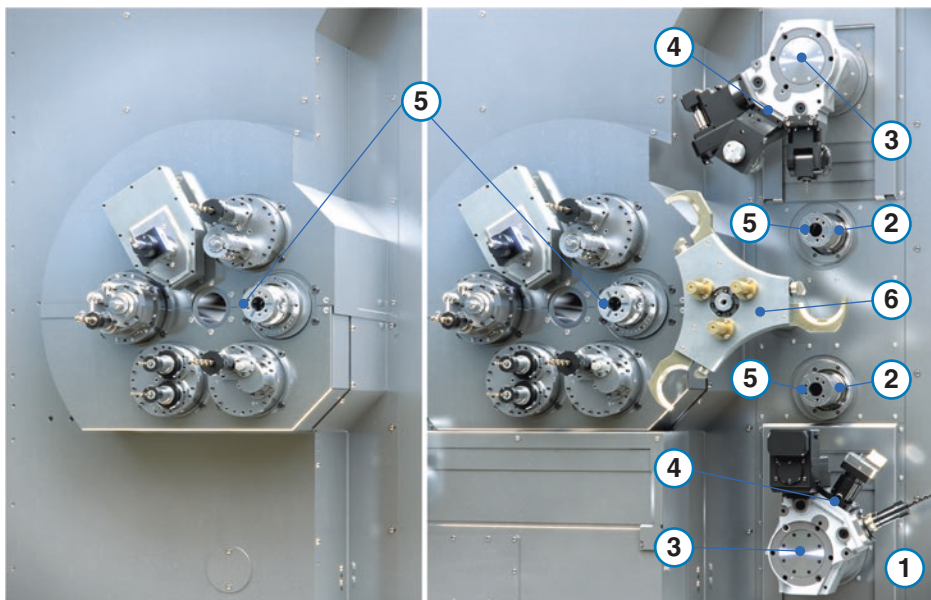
Antriebskasten der Baureihe SCX als 7-Spindler (links) und als 9-Spindler mit zusätzlichen Bearbeitungsspindeln für eine erweiterte Rückseitenbearbeitung (rechts). [Bildquelle: Schütte]
